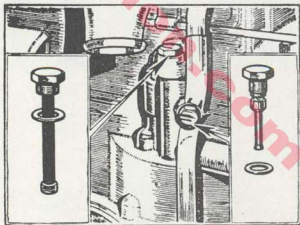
Emplazamiento del lubricador de los engranajes propulsores de la bomba de inyección con su filtro, en el lado izquierdo del bloque-motor.
